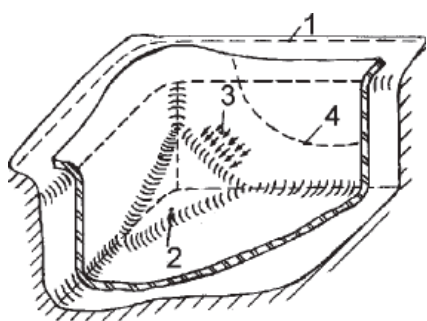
Положення заготовки в матриці перед початком другого етапу деформування:
